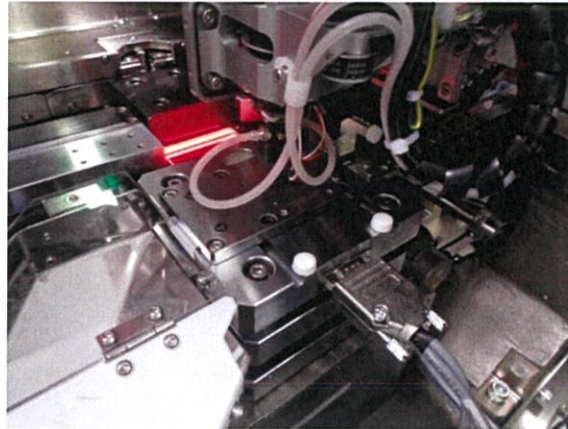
(ข) แสดงเครื่องมือ Cutting Tool MJJ
